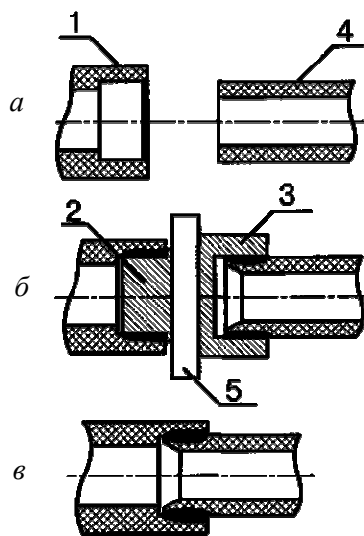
Схема зварювання труб нагрівальним інструментом:
